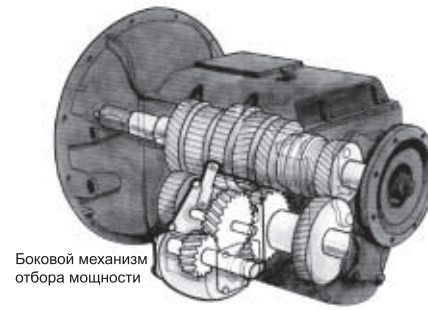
Шестерни должны надлежащим образом зацепляться с приводом MOM коробки передач.
